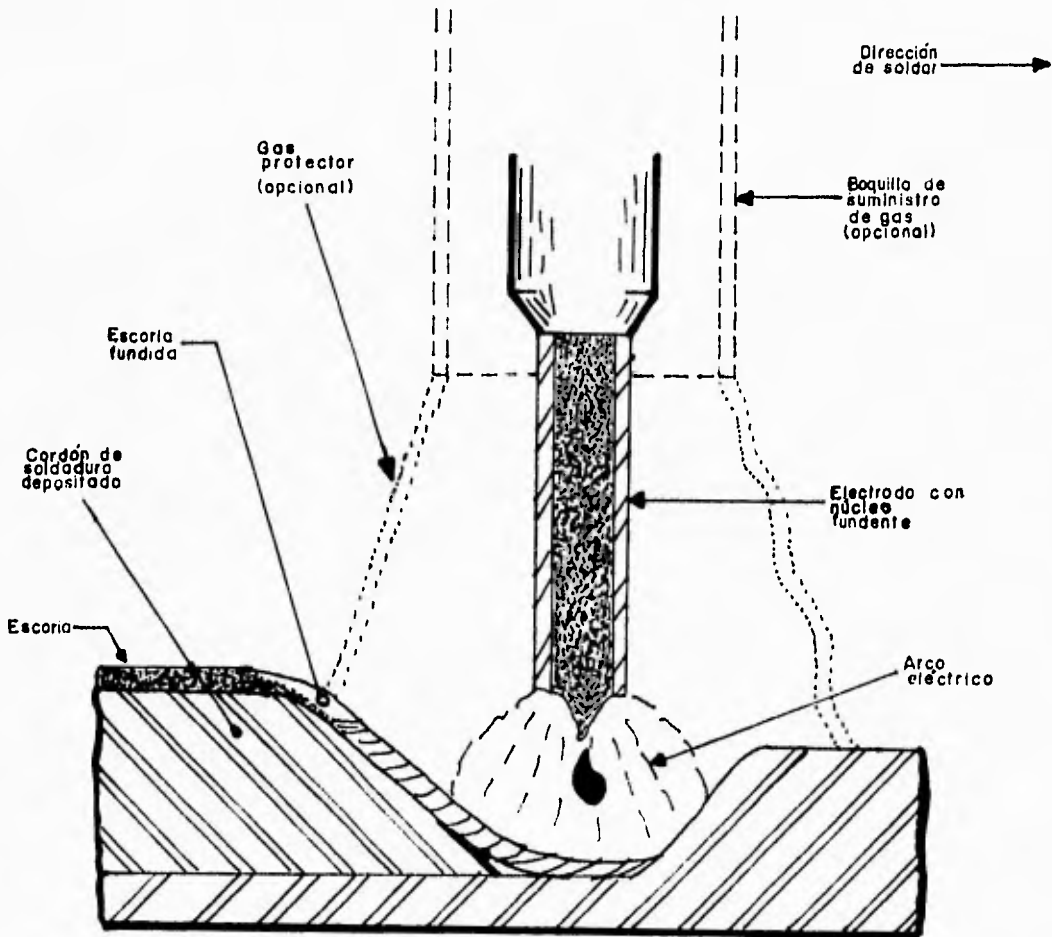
Soldadura por arco con núcleo fundente (FCAW)
